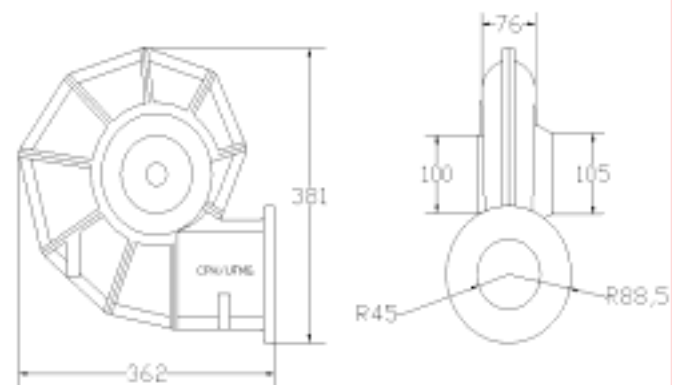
Dimensões em mm do molde confeccionado na CPH-UFMG.
